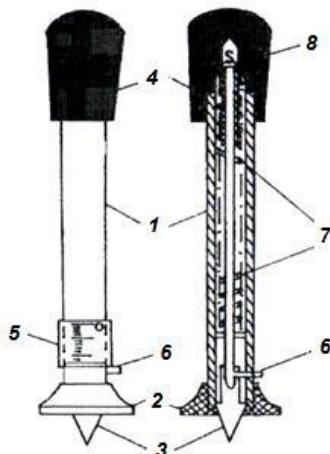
Мікропенетрометр MB-2: 1 – корпус; 2 – опорний диск; 3 – плунжер; 4 – ручка; 5 – циліндричний повзун; 6 – шпилька з'єднання плунжера зі штоком; 7 – пружина; 8 – гайка регулювання
